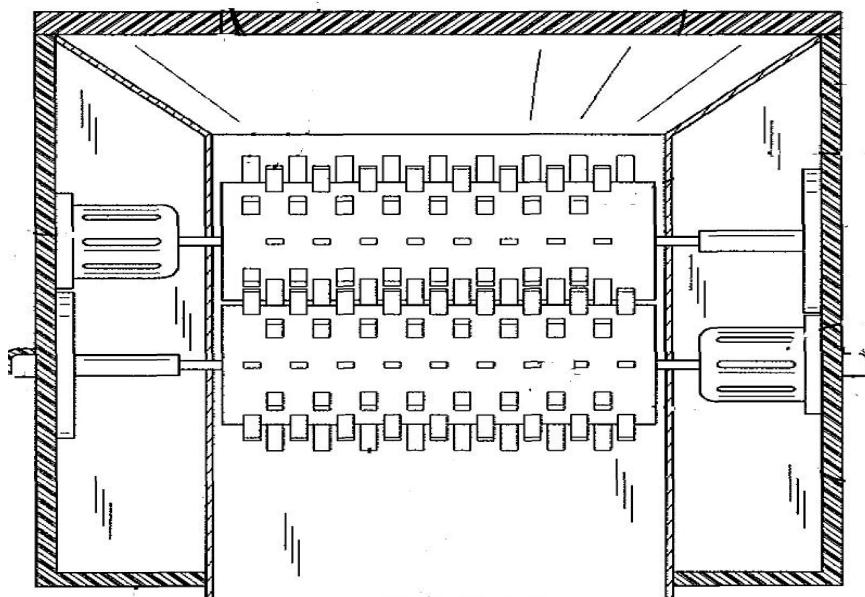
Shredding machine* de Kiyoshi Inoue (1983)
